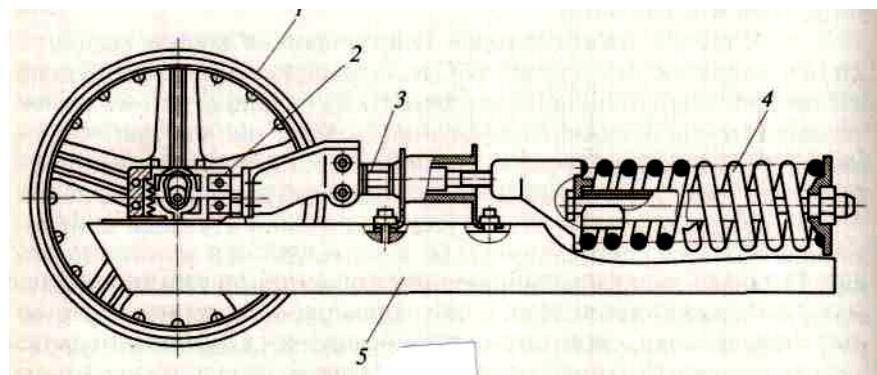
Схема установки направляющего колеса на ползуне:
